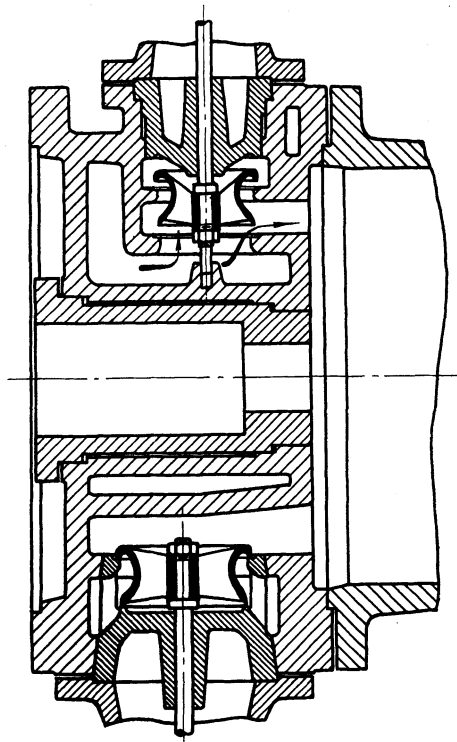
Ventilsteuerung (Ein- und Auslaßventil).
